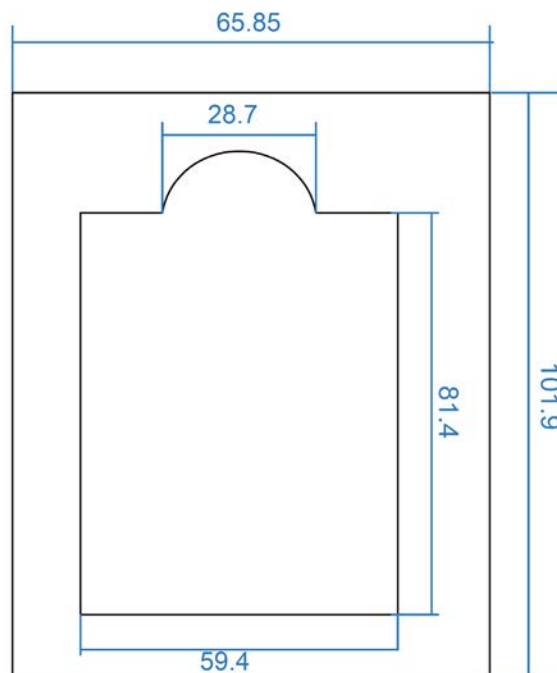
Внешний вид панели управления и габаритные размеры
